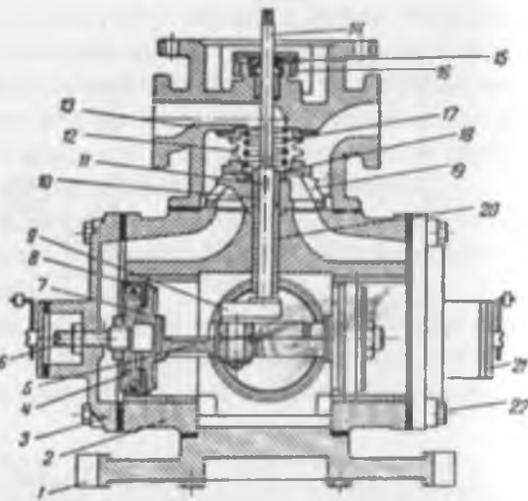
Поршневой счетчик жидкости: 1 – крышка нижняя; 2 – корпус измерителя; 3 – крышка боковая; 4 – кольцо прижимное; 5 – кулиса; 6 – винт регулировочный; 7 – поршень; 8 – манжета; 9 – коленчатый вал; 10 и 20 – втулки; 11 – шпонка; 12 – сильфон; 13 – корпус золотника; 14 – валик; 15 – манжета уплотнительная; 16 – гайка; 17 – шруц; 18 – кольцо уплотнительное; 19 – золотник; 21 – крышка упора кулисы; 22 – болт М8
